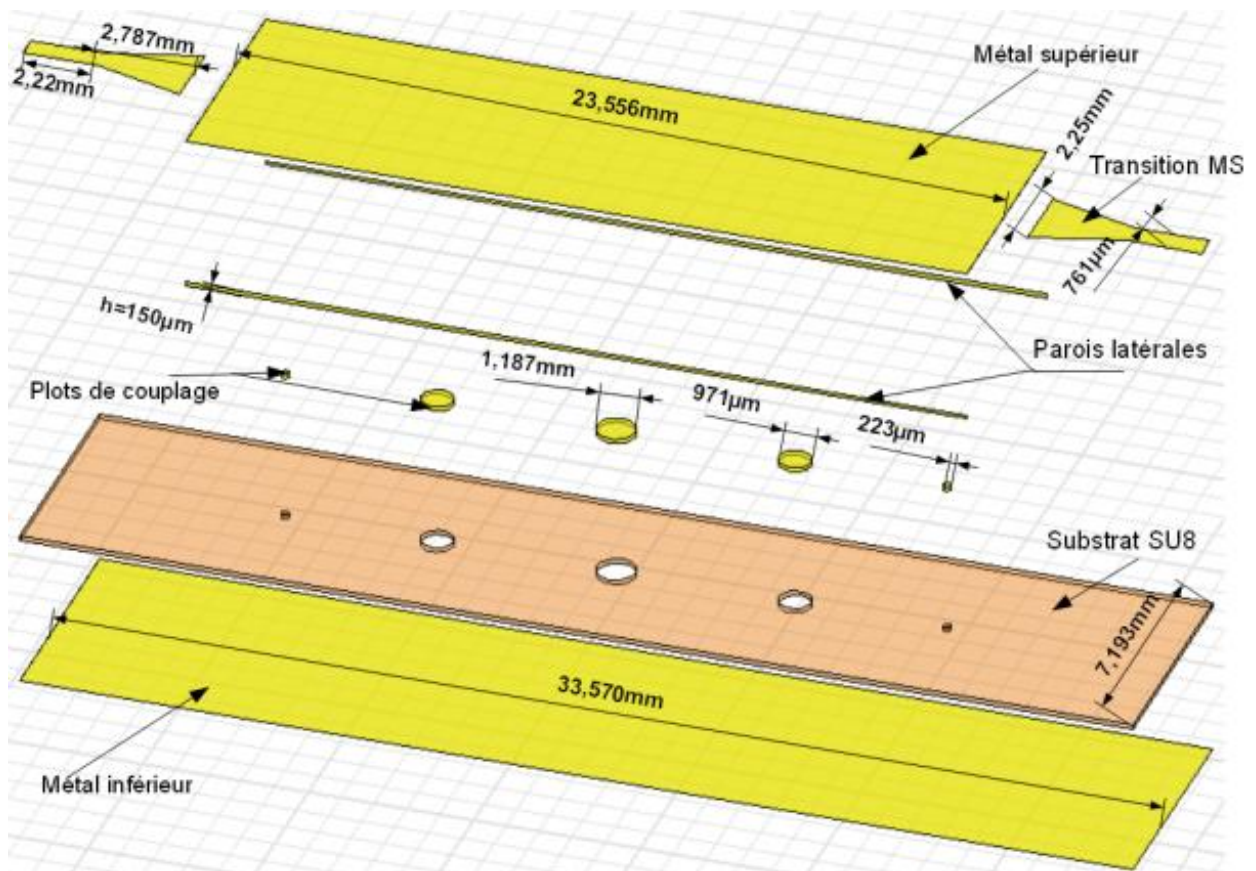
Vue éclatée avec ses dimensions du filtre SIW simulé.
